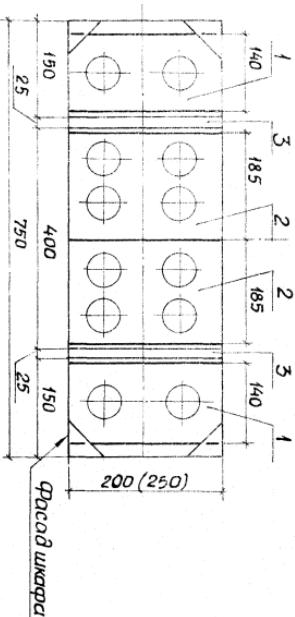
Пример установки блоков из патрубков для напольного шкафа шириной 250мм.
